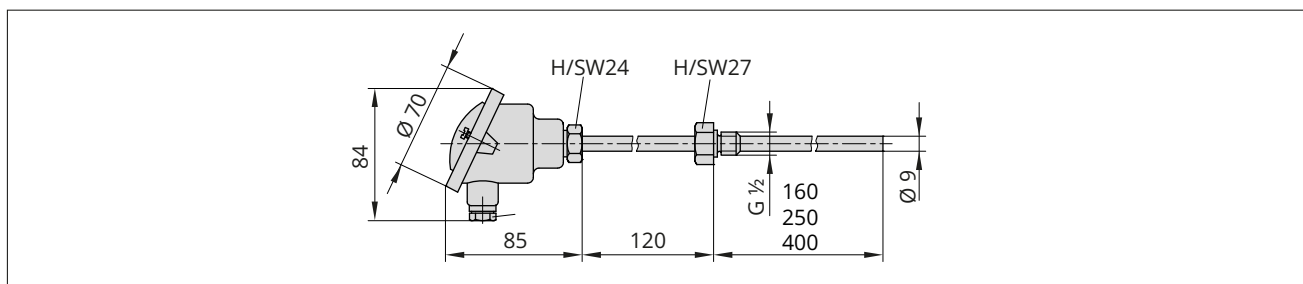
Maße in mm · Einschraubsensor Typ 5207-4x
